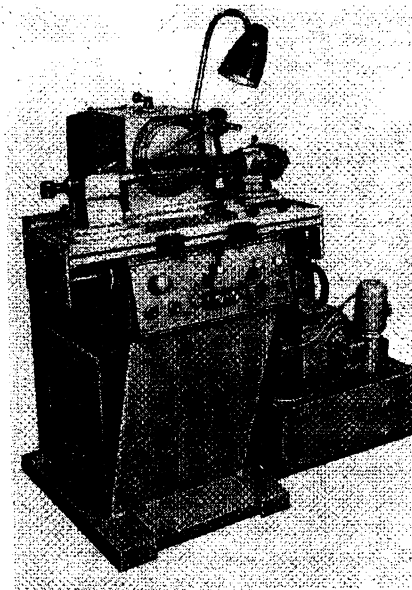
Универсально-заточной станок ТЧУ-Гл для алмазной глубинной заточки круглых пил, фрез, ножей
